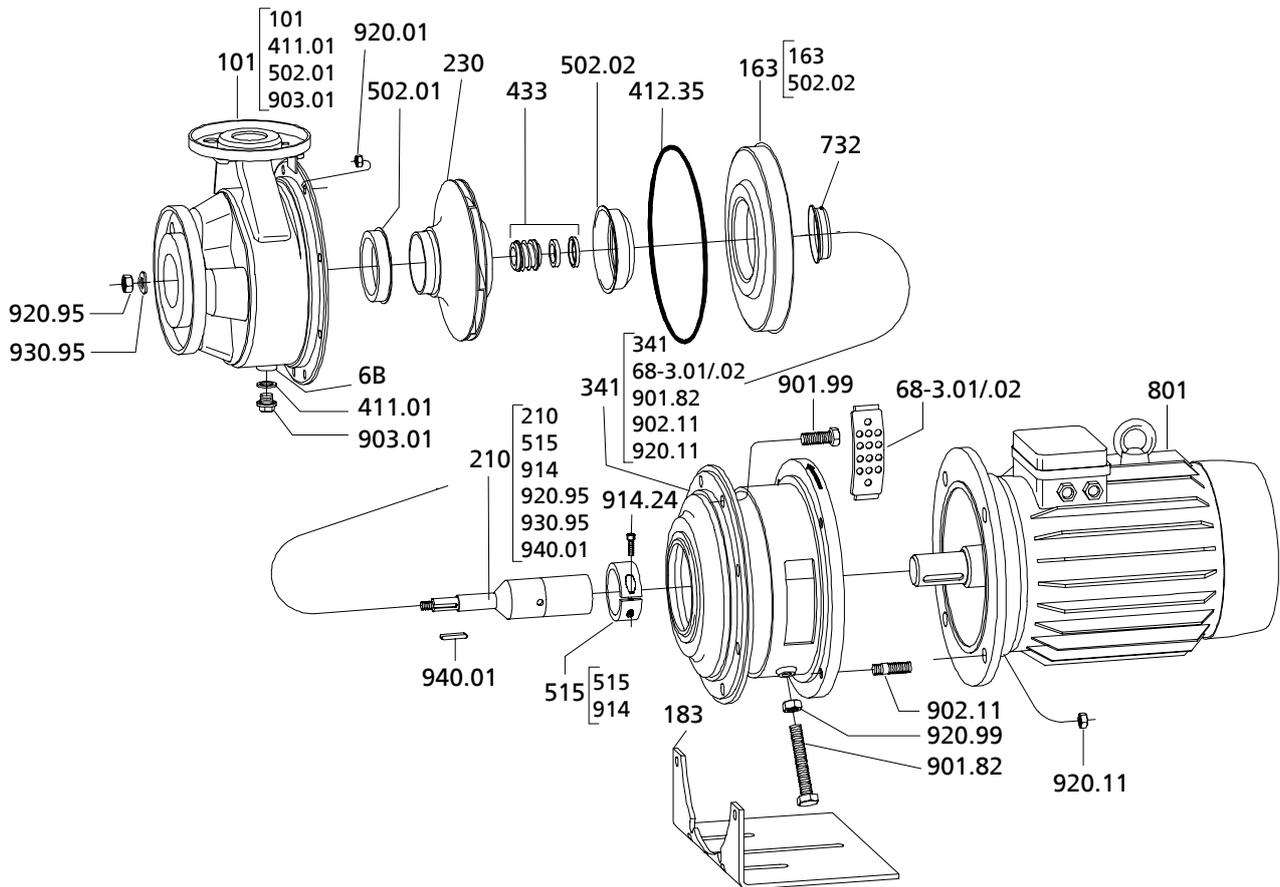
Explosionszeichnung Ausführung mit Welleneinheit 25.1
